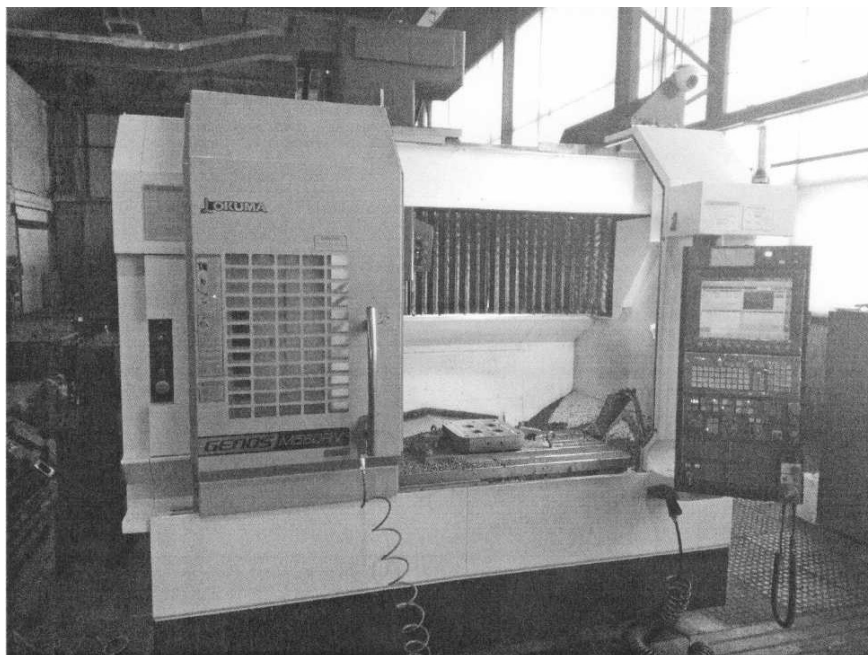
Вертикально-фрезерувальний обробний центр з ЧПУ OKUMA Genos M560RV
